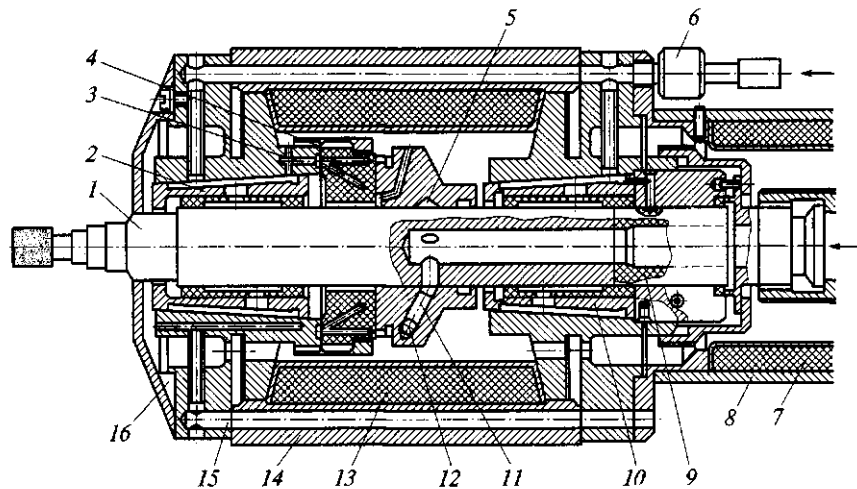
Пневмощпиндель прецизионного внутришлифовального станка: 1 — вал; 2, 10 — радиальные опоры; 3 — подводящее отверстие; 4 — подпятник; 5 — кольцевая канавка; 6 — штуцер; 7, 8, 13 — глушители; 9 — втулка; 11 — радиальный канал; 12 — сопло; 14 — корпус; 15 — канал; 16 — паз для охлаждения
